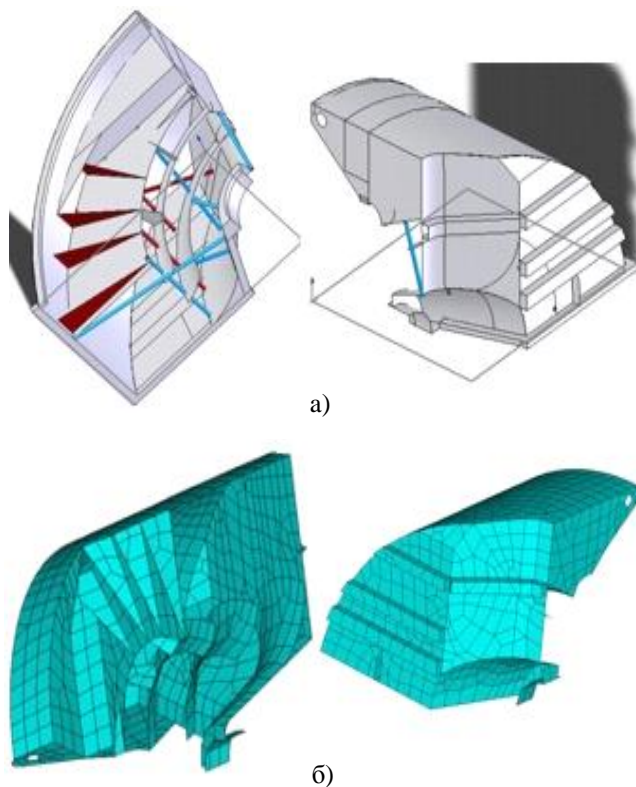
а — четвертина кришки корпусу турбіни К-500 (модернізована конструкція з жорсткістю); б — скінченно-елементна модель четвертини кришки корпусу турбіни К-500 (модернізована конструкція з жорсткістю)
